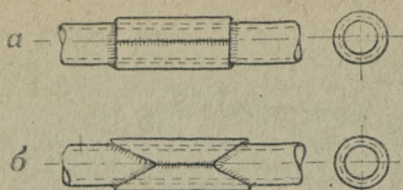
Ремонт трубчатой конструкции при помощи приварки накладок
